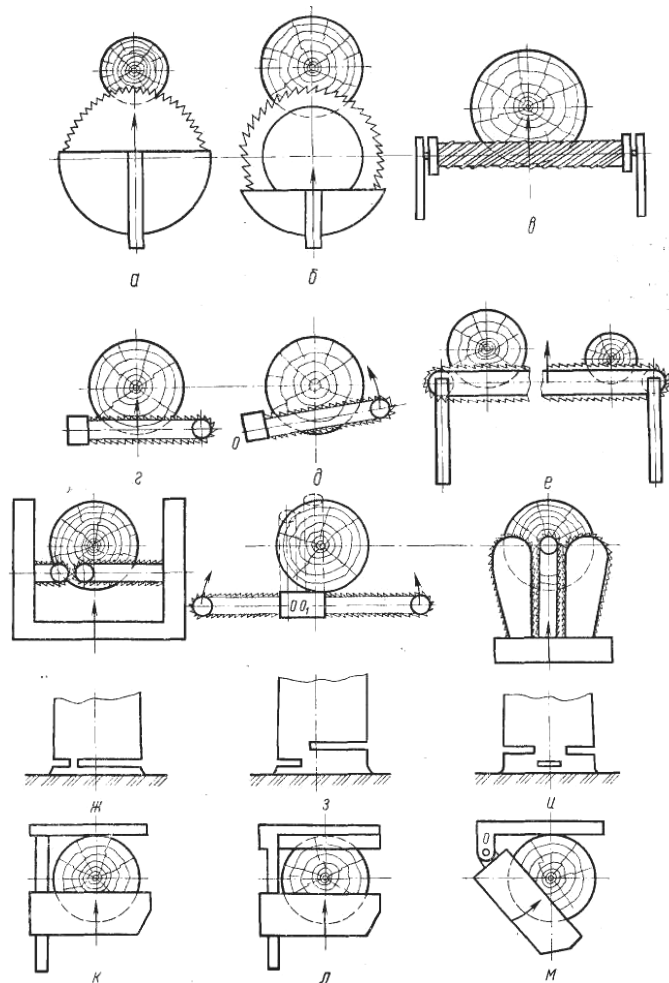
Схеми зрізаючих механізмів: а - дискова пила; б - дискова фреза; в - циліндрова фреза; г, д - ланцюгові пили; е - пильний бар; ж, з - двохшинні ланцюгові зрізаючі механізми: и - трьохшинний ланцюговий зрізаючий механізм; к, л, м - клинові ножі
